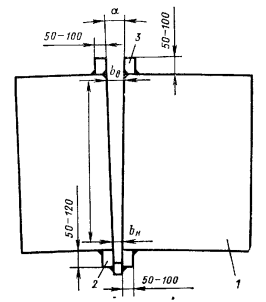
Общий вид стыка, подготовленного к электрошлаковой сварке:
